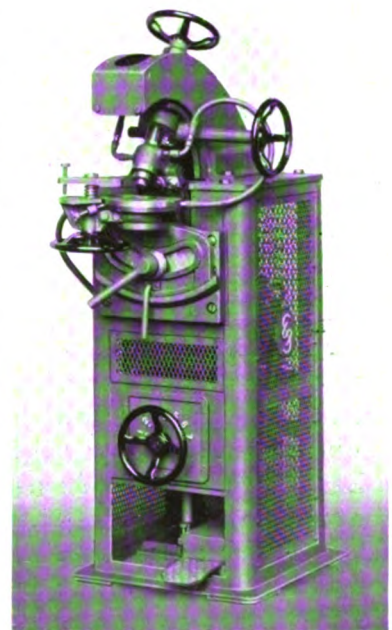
Edelstahl-Aufschweißmaschine.
